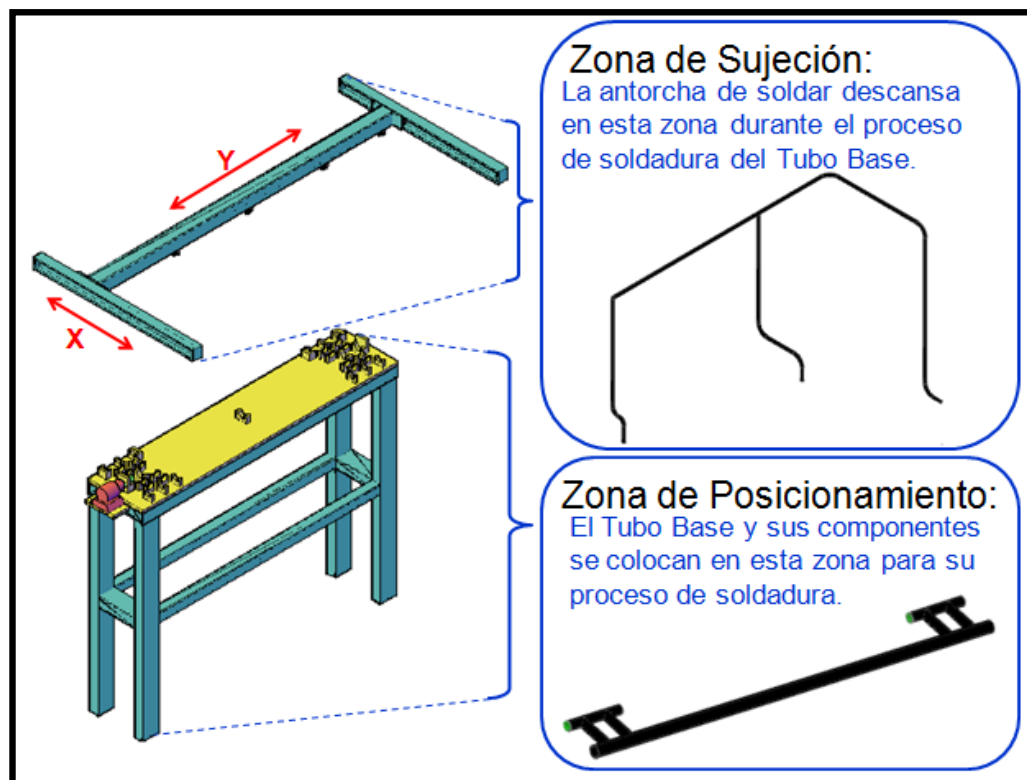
Esquema de la nueva cabina de soldar del Tubo Base.
